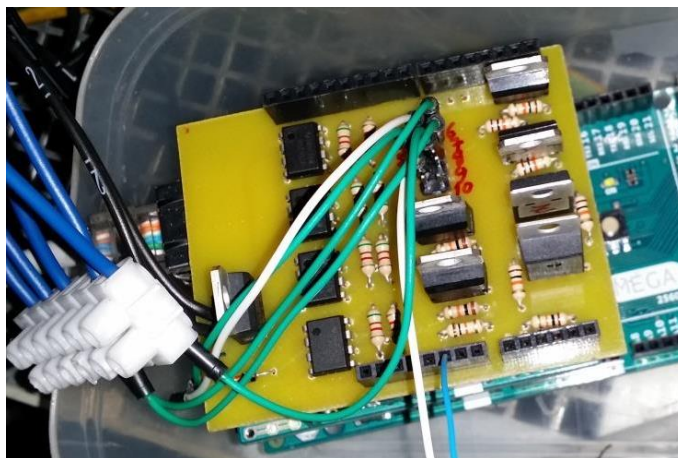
Circuito da Figura 4.22, instalado em PCB.
